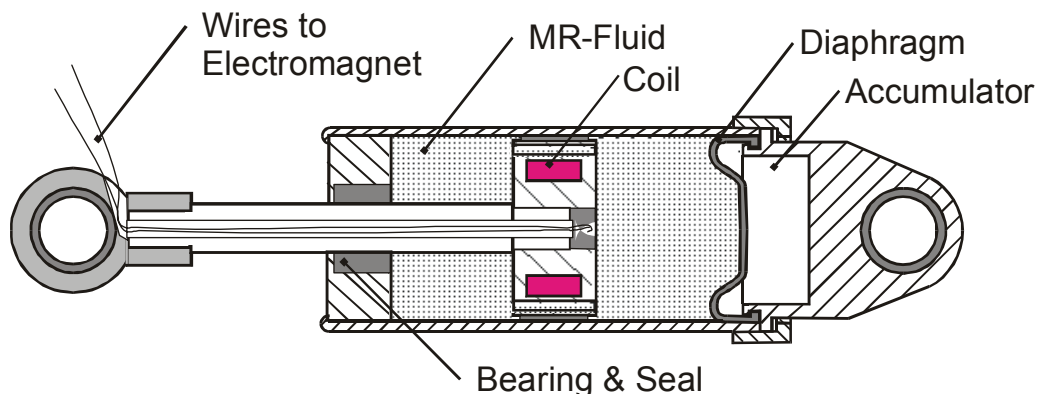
MRF-Schwingungsdämpfer RD-1005-1, Lord Corporation [90]
